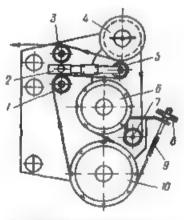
Кинематическая слема каретън бандажировочного станка с механизмом натяжения
